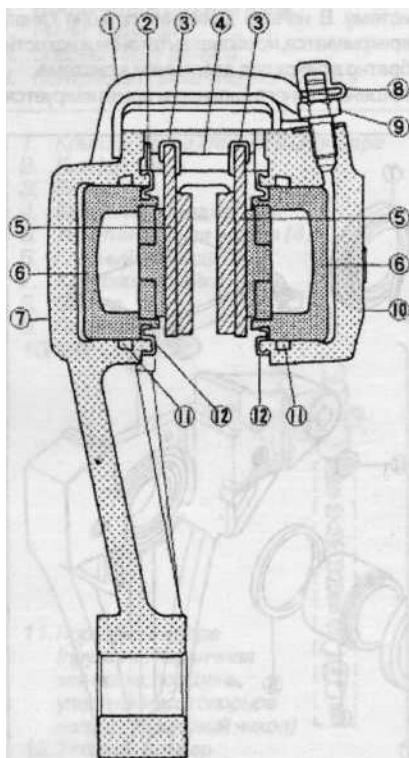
Зв Двухпоршневой неподвижный суппорт в разрезе
